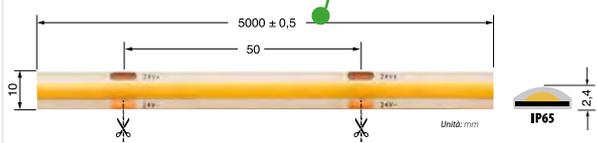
FOTO CON DIMENSIONI PASSO E GRADO DI PROTEZIONE
